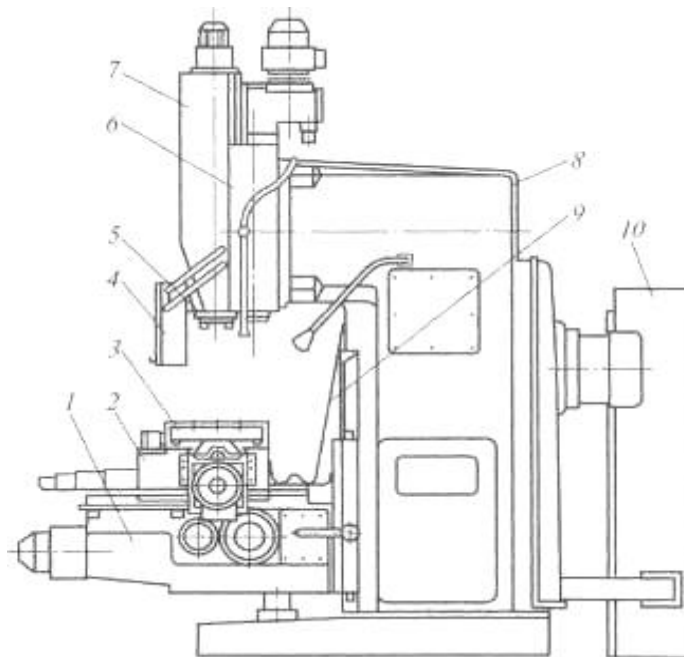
Компонування вертикально-фрезерного консольного верстата
